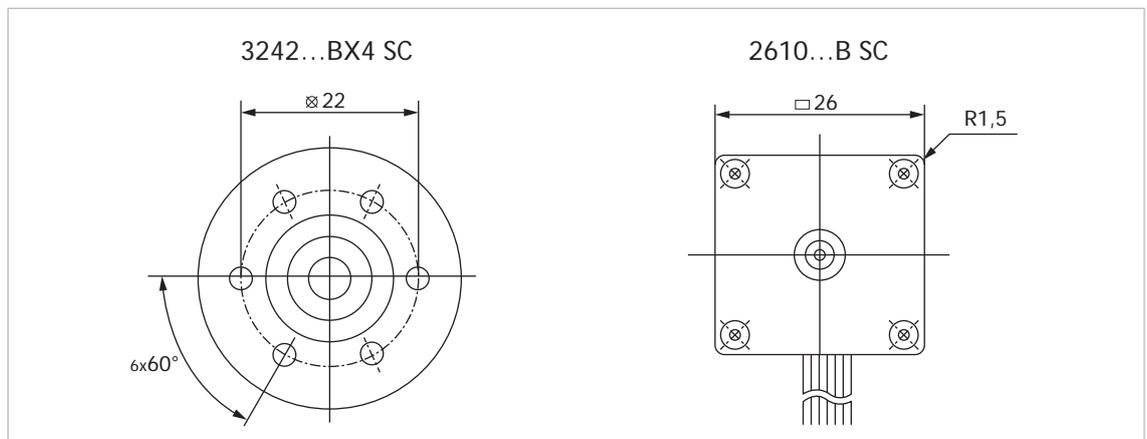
Vergleich runder Flansch / quadratischer Flansch
